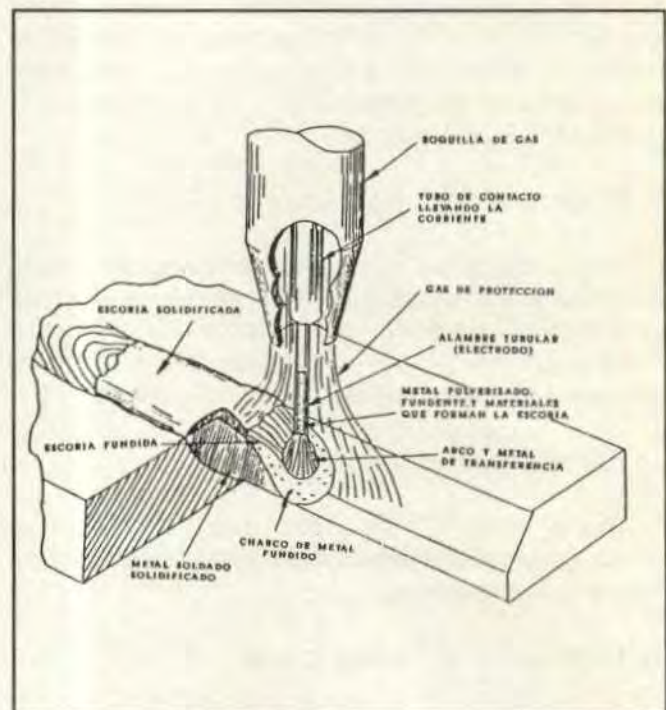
Detalle de la Soldadura F.C.A.W.
